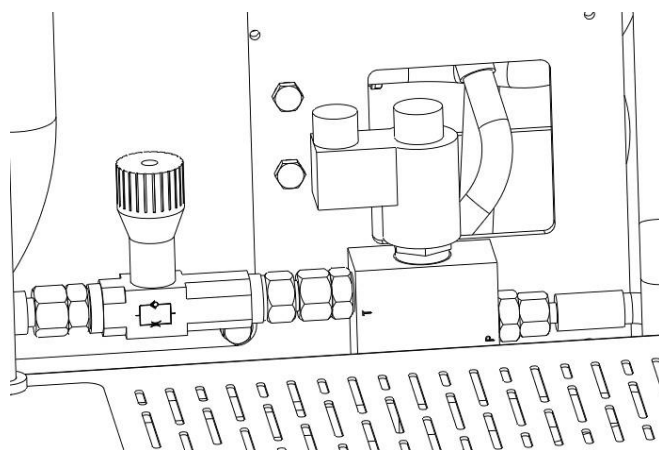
Обратный дроссельный клапан блокирующий механизм установки в выдвинутом положении
